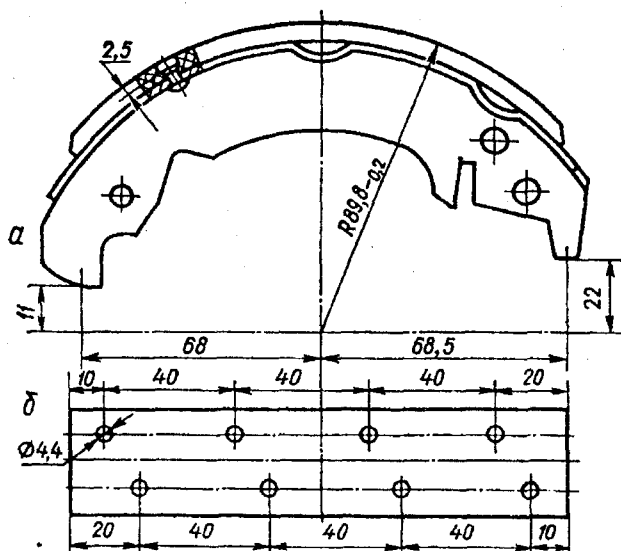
Крепление фрикционных накладок тормоза заклепками: а – колодка тормоза в сборе; б – фрикционная накладка в развертке (размеры 2,5 и 89,8–0,2 указаны после шлифовки)
